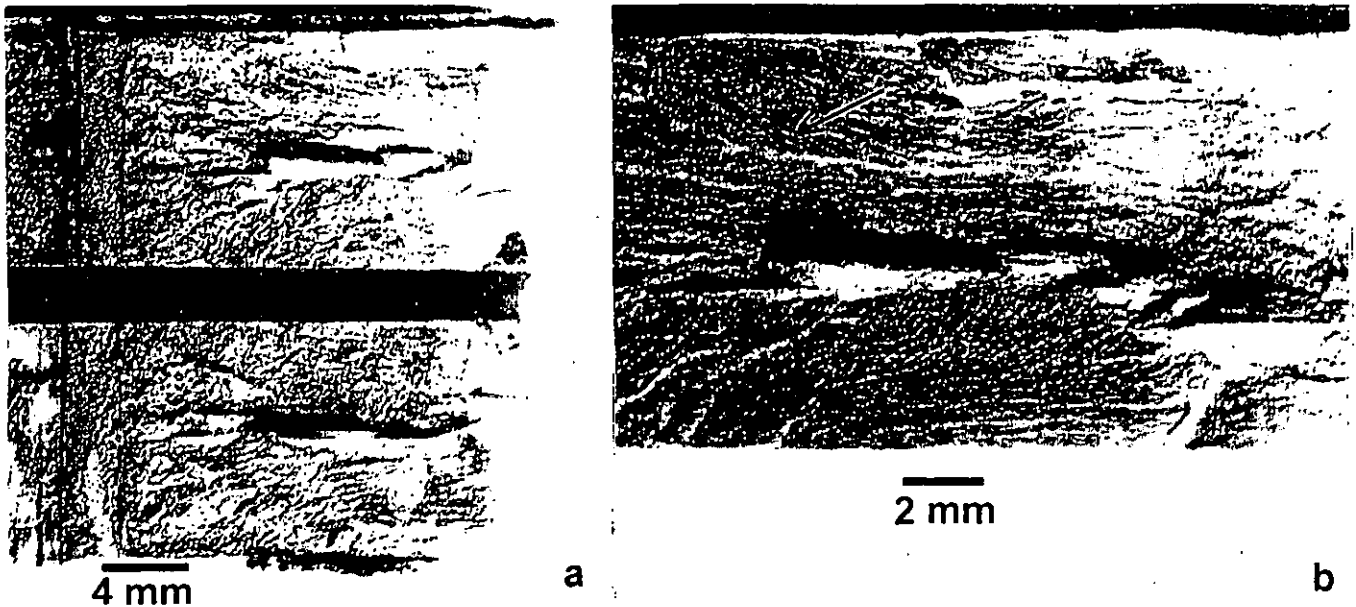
Superficies de fractura. (a) Fractura sin remover los productos de corrosión en la superficie. (b) Superficie limpia.
